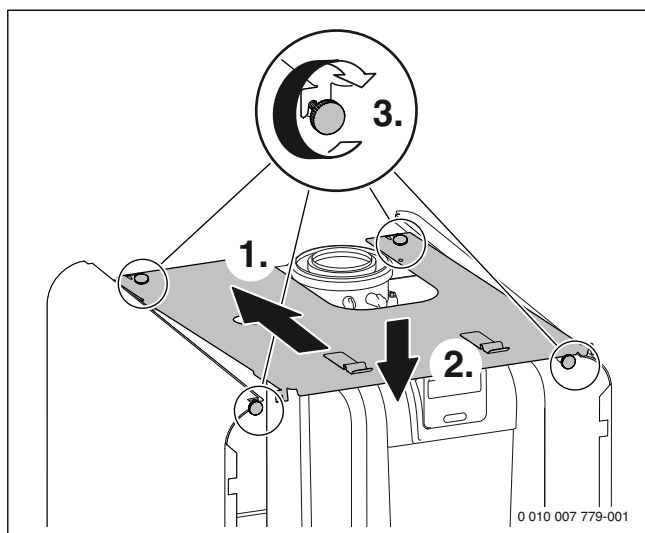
Glisser le carénage supérieur vers l'arrière et fixer à l'avant et l'arrière avec les 4 vis
